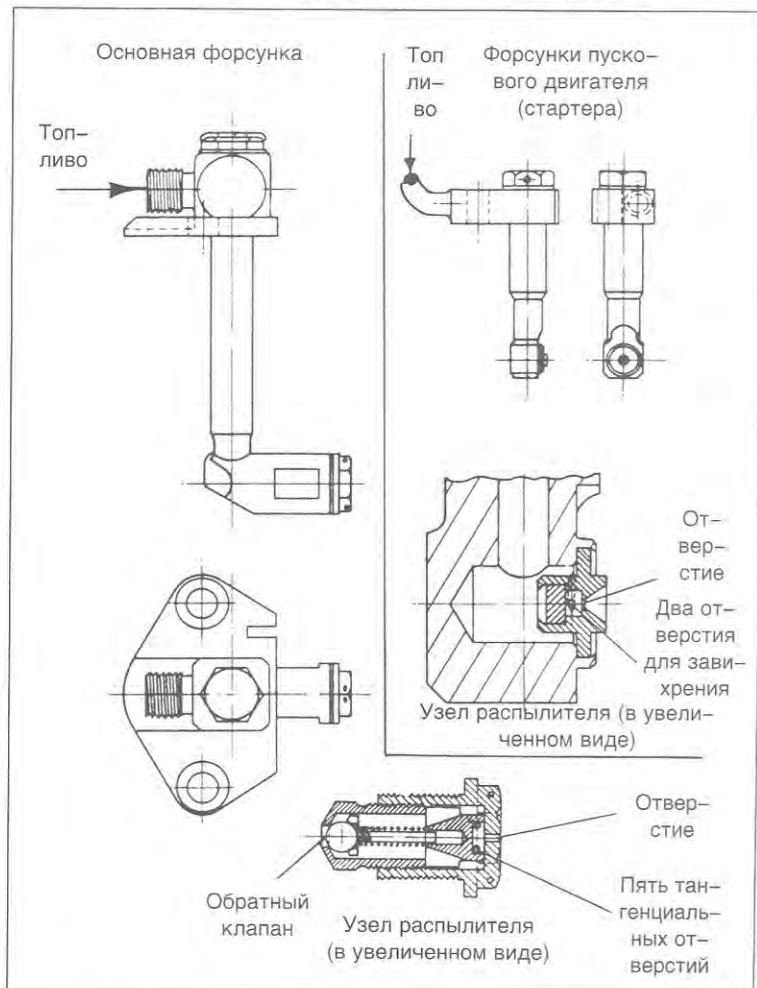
Основная и пусковая форсунки для двигателя BMW 109-003 A
